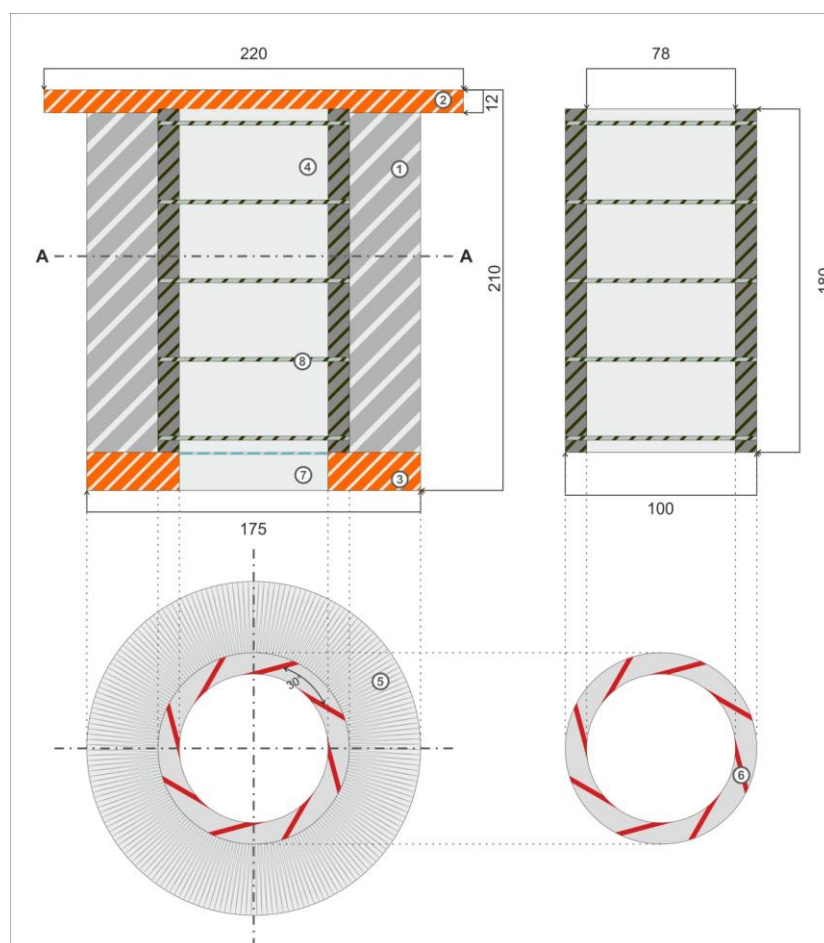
Устройство воздухоподготовки для мобильных сельскохозяйственных агрегатов.
